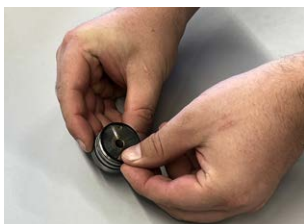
Anbringen des zweiten O-Rings an der Einsatzbuchse
